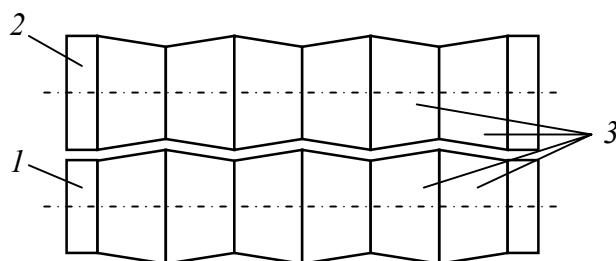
Схема валків вальців згідно з пат. України № 242 U [119]: 1, 2 – кінцеві циліндричні ділянки бочок валків; 3 – конічні ділянки бочок валків
